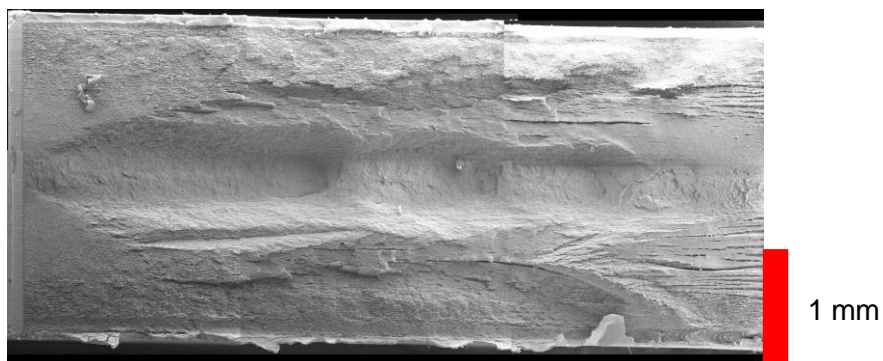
Imatge composta de la superfície de fractura de Bioblend 6 zona lateral
